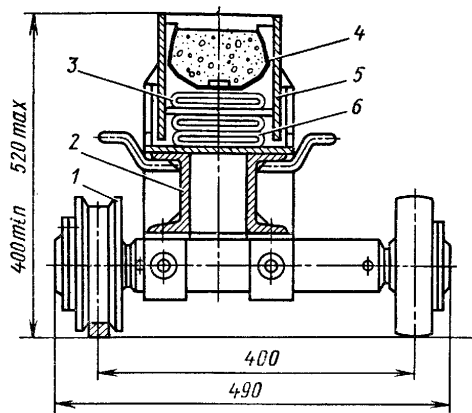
Флюсовая подушка для сварки внутренних продольных швов обечаяк:
